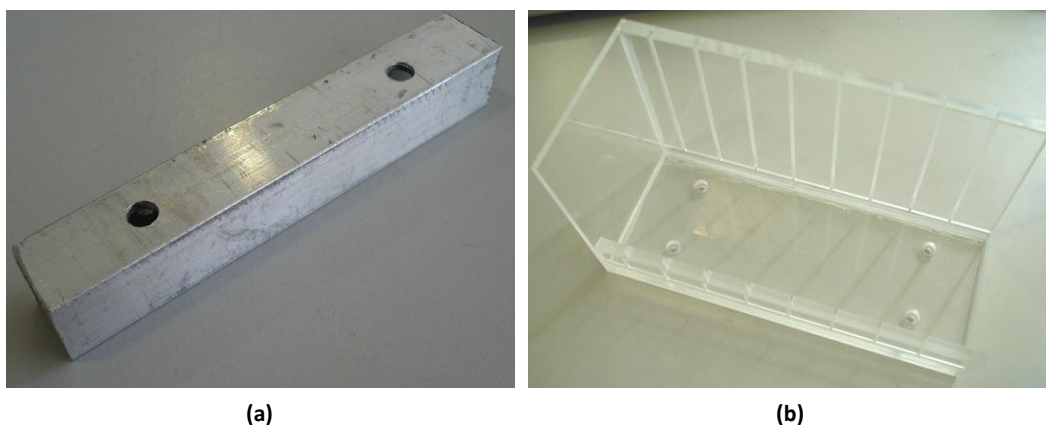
(a) Suporte de alumínio para elevação da caixa de suporte das placas; (b) Caixa em acrílico para suporte e protecção das placas.
